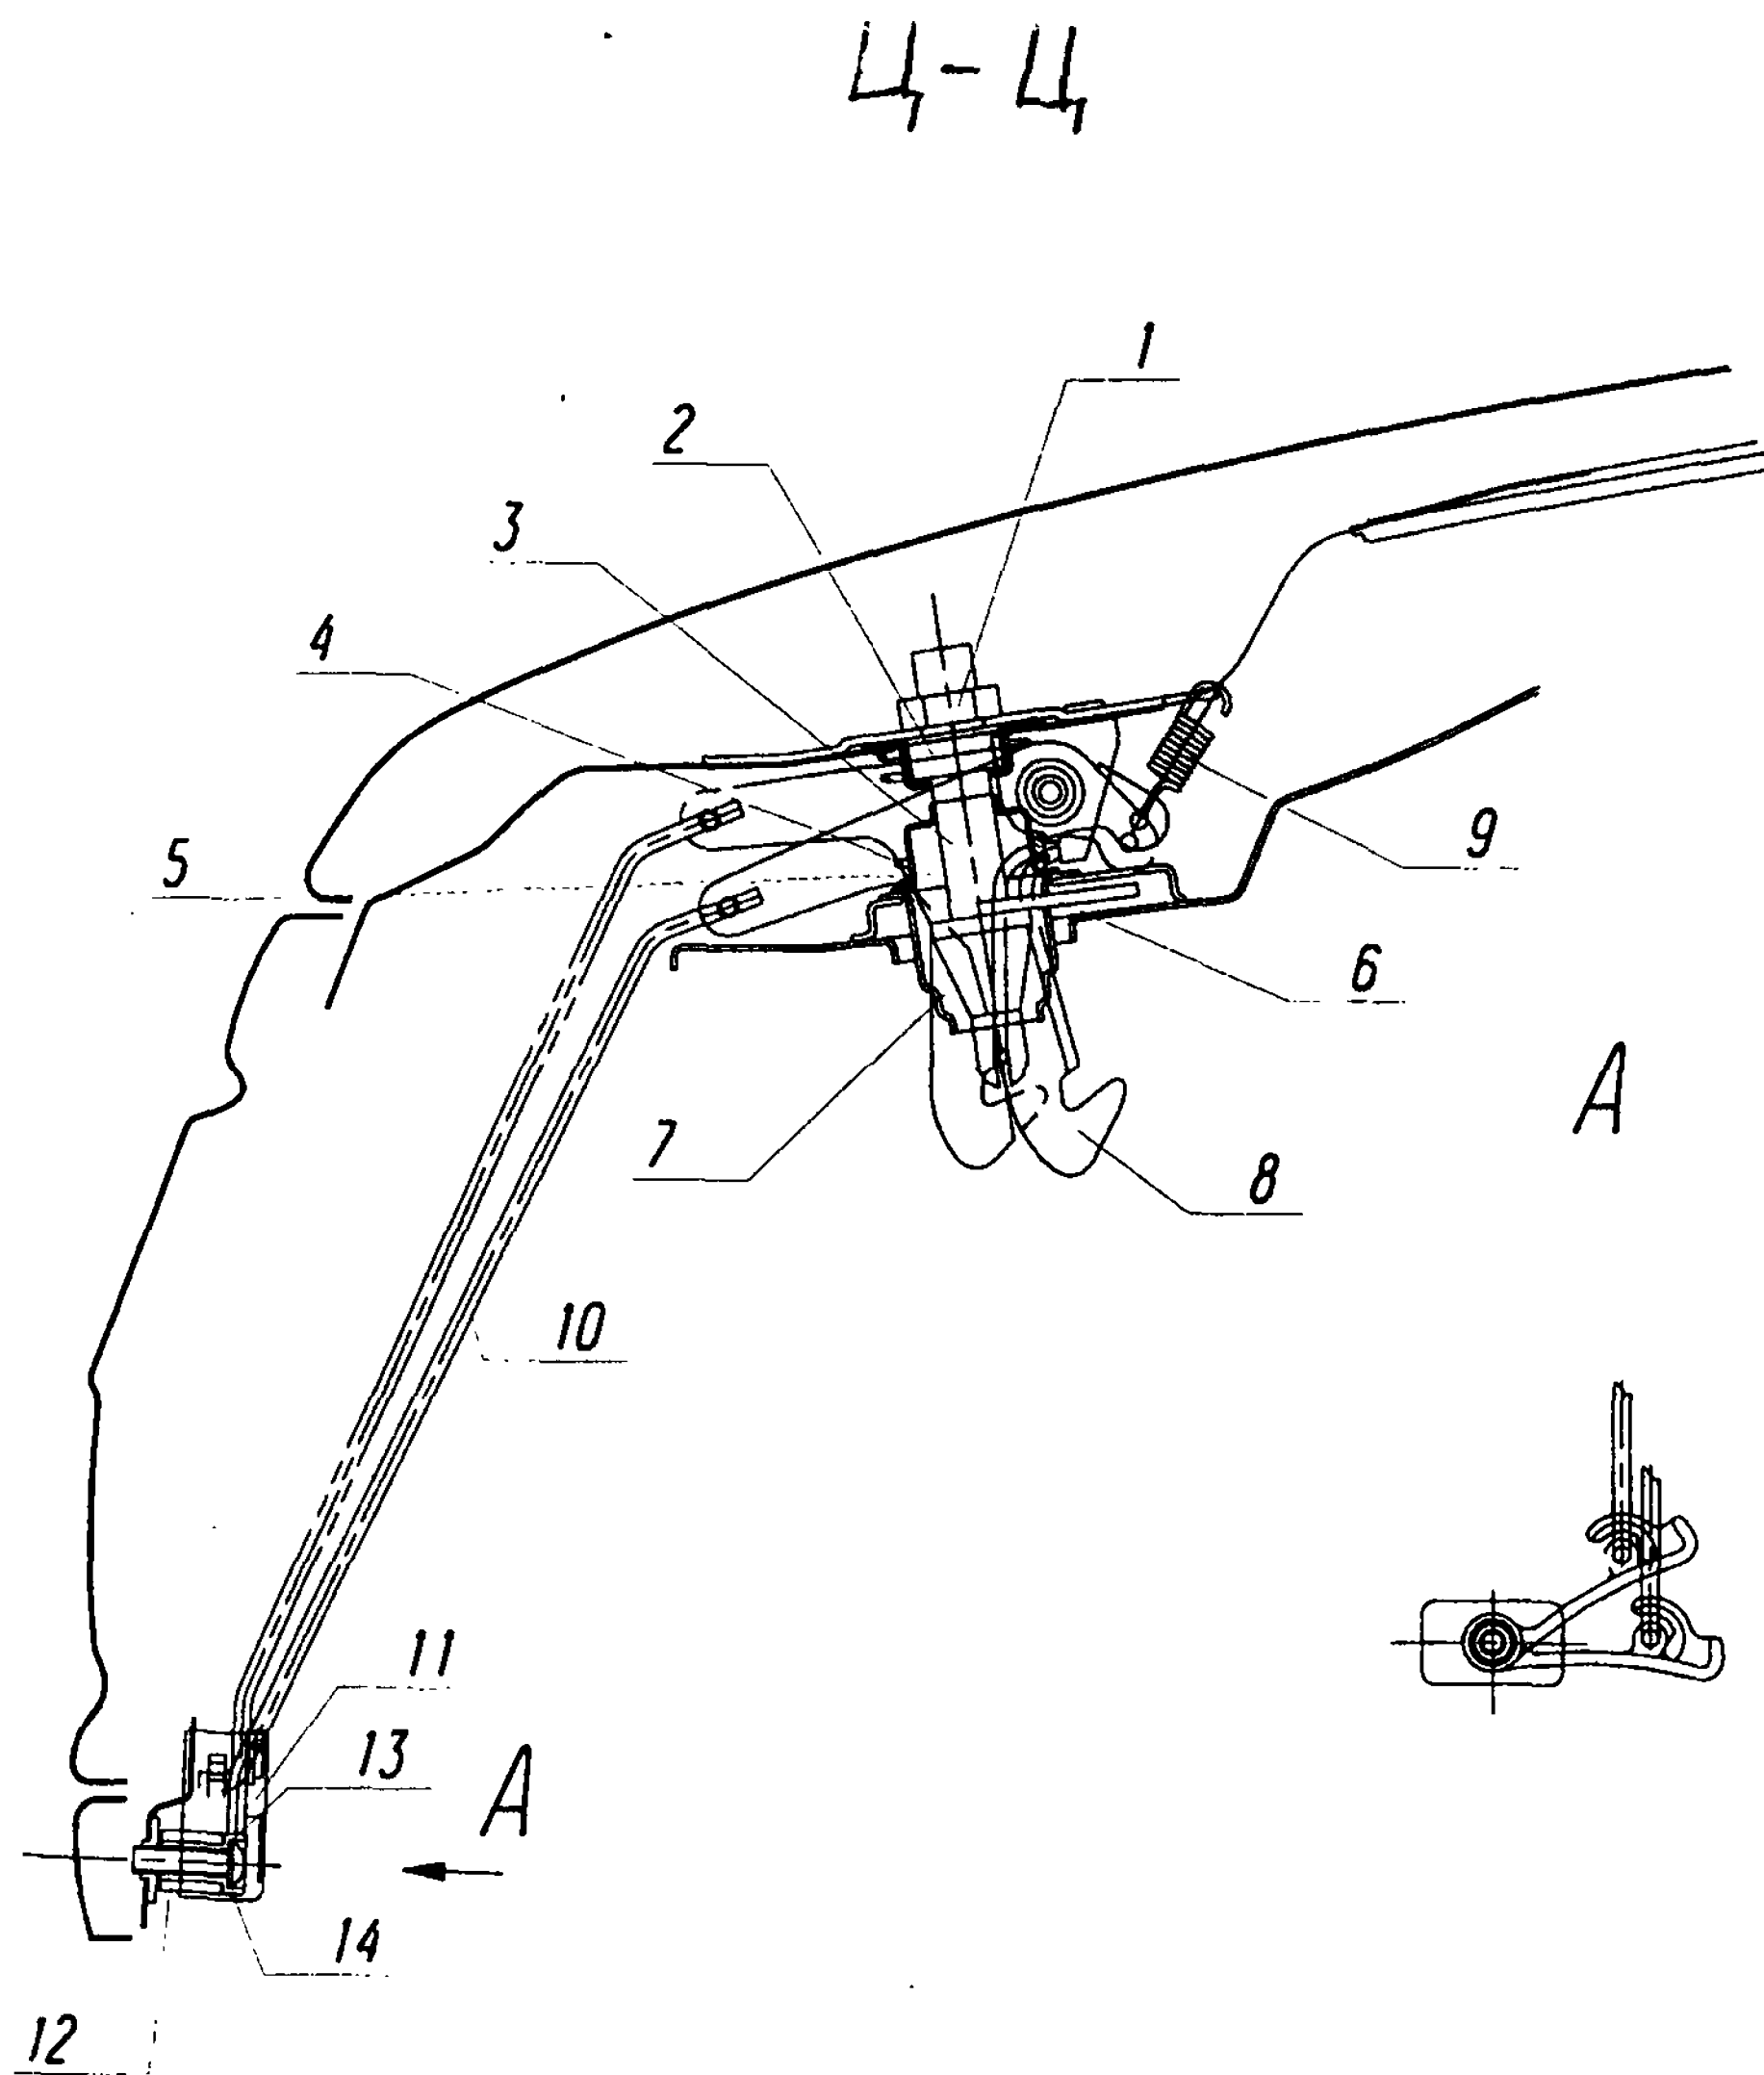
Замок капота и предохранительный крючок: 1 - контргайка; 2 - гайка неподвижная с гайкодержателем; 3 - штырь; 4 - пружина штыря; 5 - фланец пружины; 6 - щеколда; 7 - направляющая штыря; 8 - предохранительный крючок; 9 - пружина предохранительного крючка; 10 - тяги привода предохранительного крючка; 11 - ручка предохранительного крючка; 12 - ось ручки предохранительного крючка; 13 - винт; 14 - шайба
